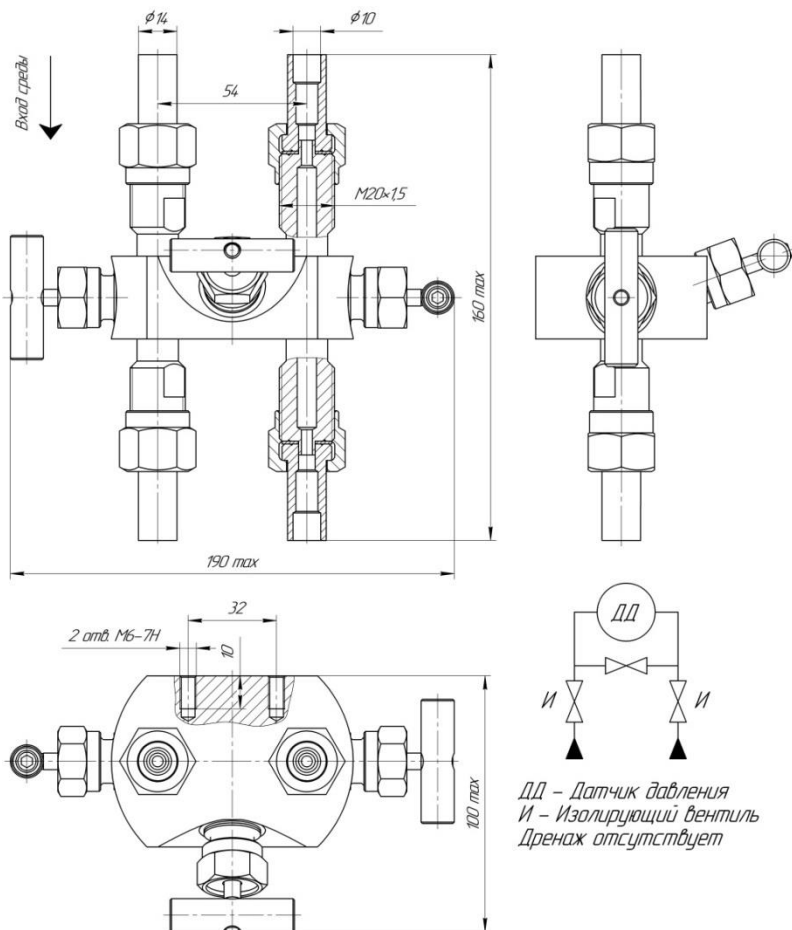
Габаритно-присоединительные размеры и гидравлическая схема 3-вентильных блоков исполнения БКНЗ-11-12С2
